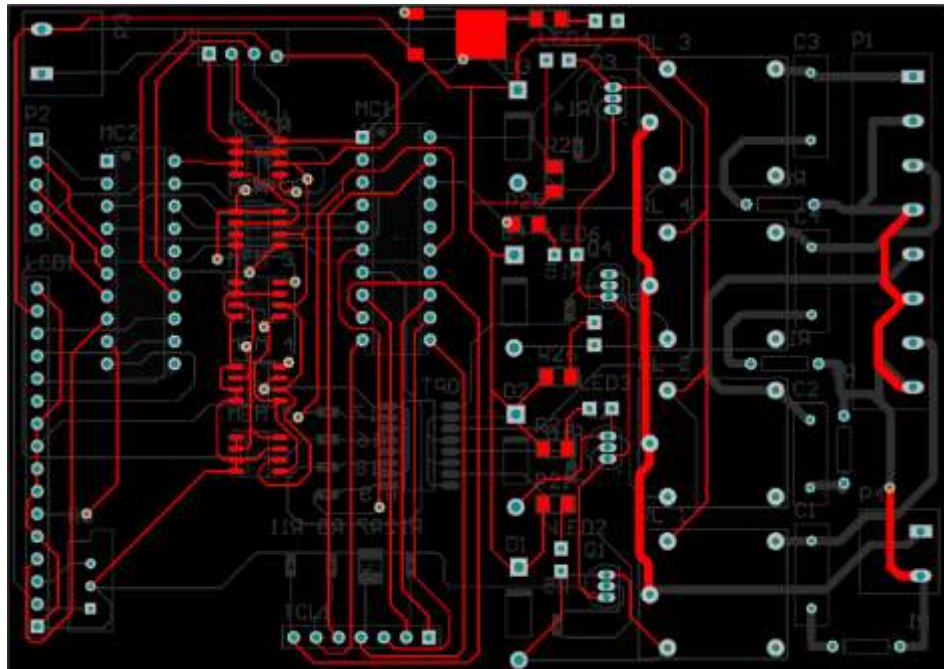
Diseño PCB Sistema Electrónico Capa Superior.
